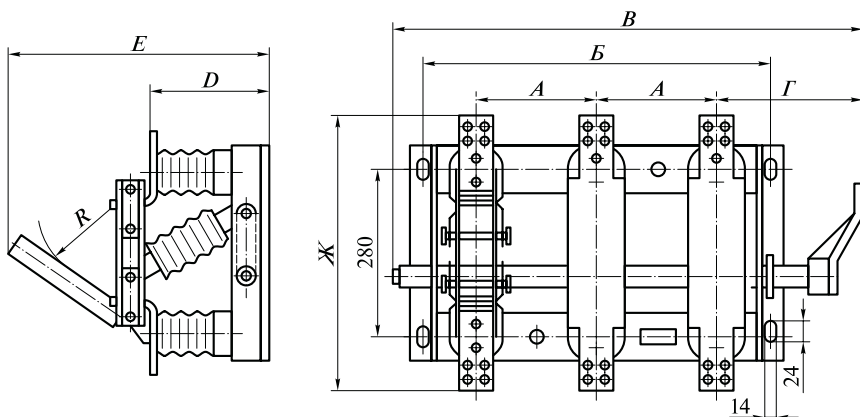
Трехполюсный разъединитель 10 кВ для внутренней установки типа РВ
